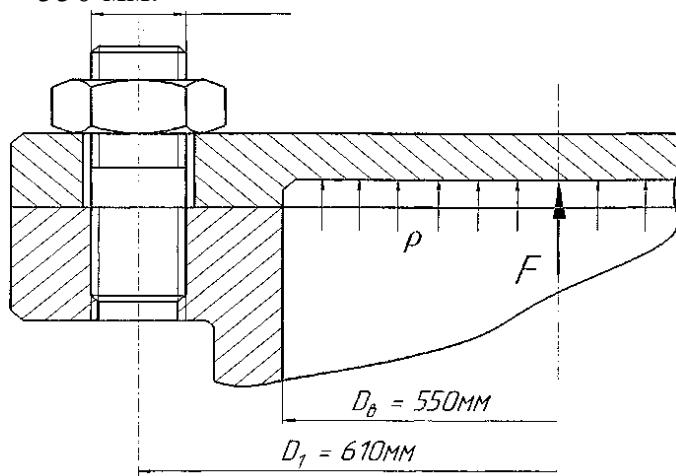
Крепление крышки к цилиндуру поршневого двигателя
